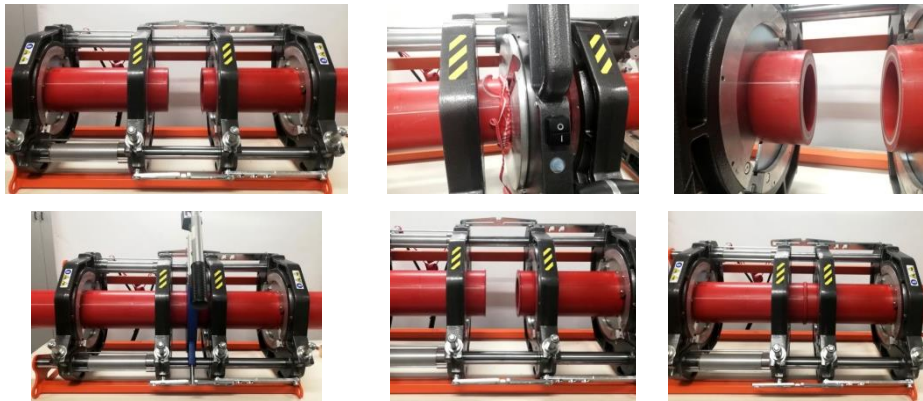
Termofusión: soldadura a tope. Parámetros
